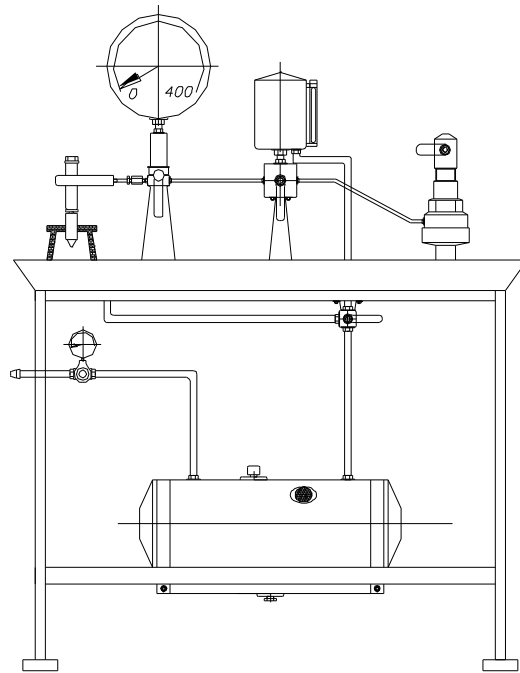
Стенд для перевірки форсунок та плунжерів модель 625
